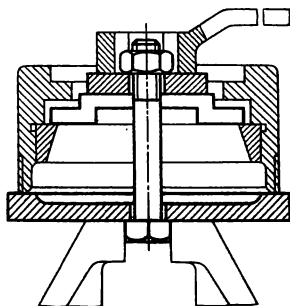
Приспособление для выпрессовки наружного кольца подшипника
